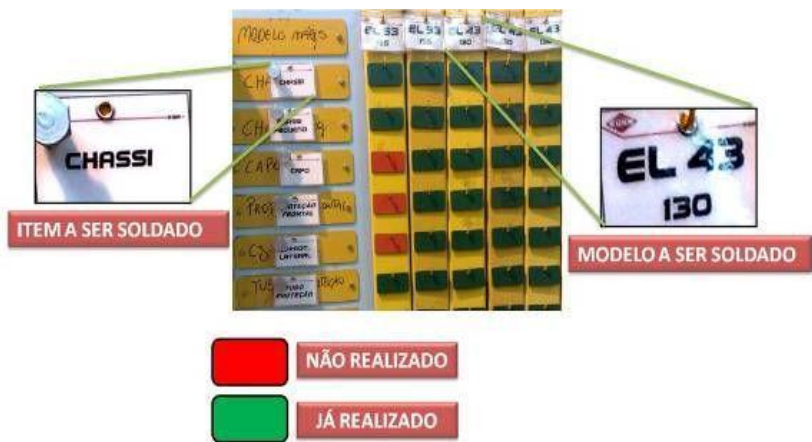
Quadro de sequenciamento da soldagem
